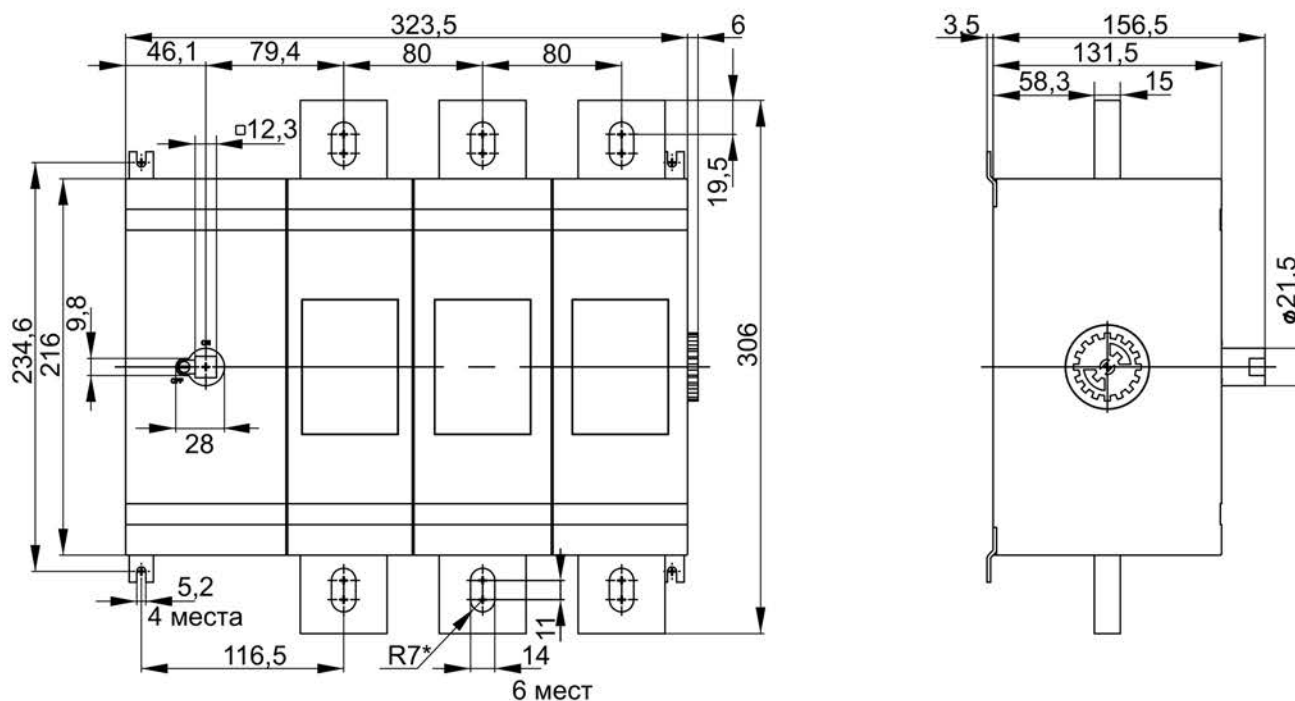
Габаритные, установочные и присоединительные размеры ВРК 1000–1600 А / Figure 4 – Overall, mounting and connection dimensions of VRK 1000–1600 A
